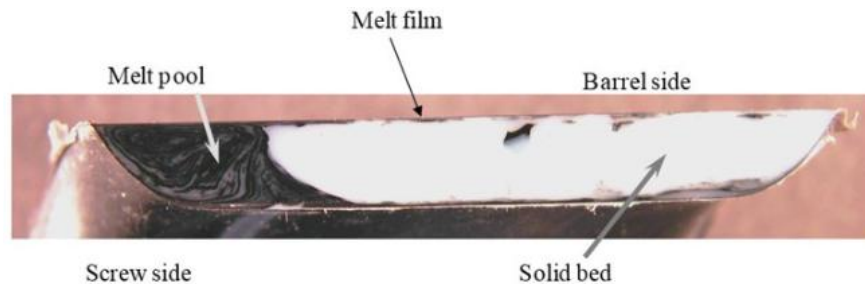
Vista en corte del detalle del canal de una extrusora. [19]
